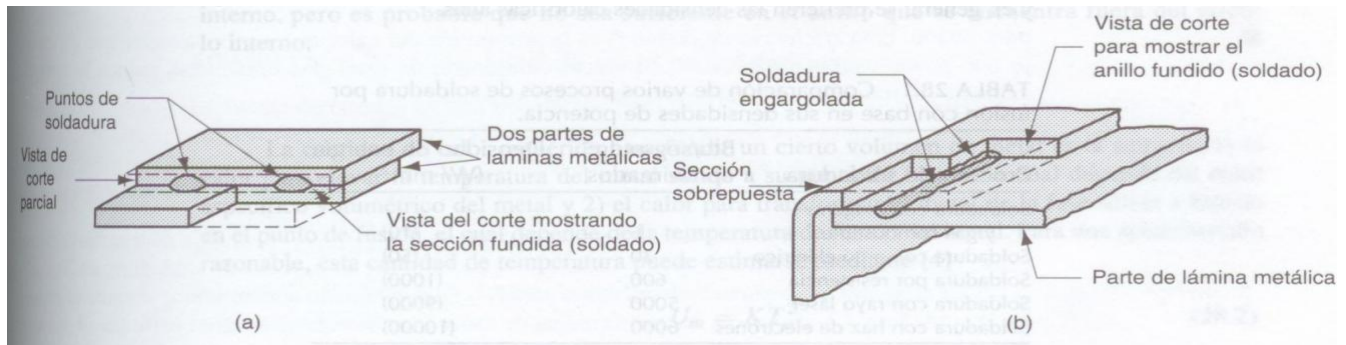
(a) Soldadura de puntos y (b) soldadura engargolada.
